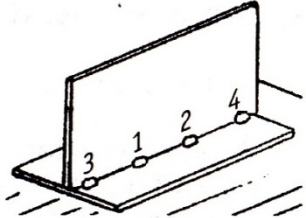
Выполнение сварки таврового соединения
